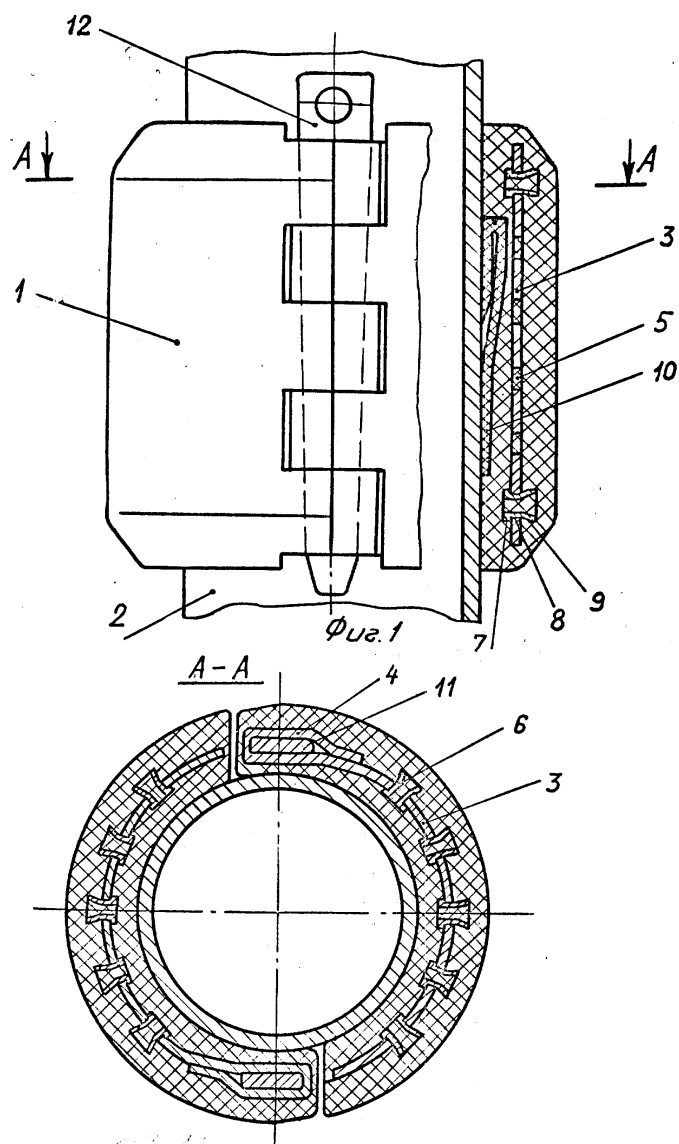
Протектор для бурильных труб: 1-оболочка, 2- бурильная труба, 3- металлический каркас, 4- петли, 5- отверстия, 6- втулка, 7 – цилиндрический буртик, 8 – цилиндрический пояс, 9- усеченный конус, 10- прокладка, 11- отверстия, 12 соединительные клинья.
